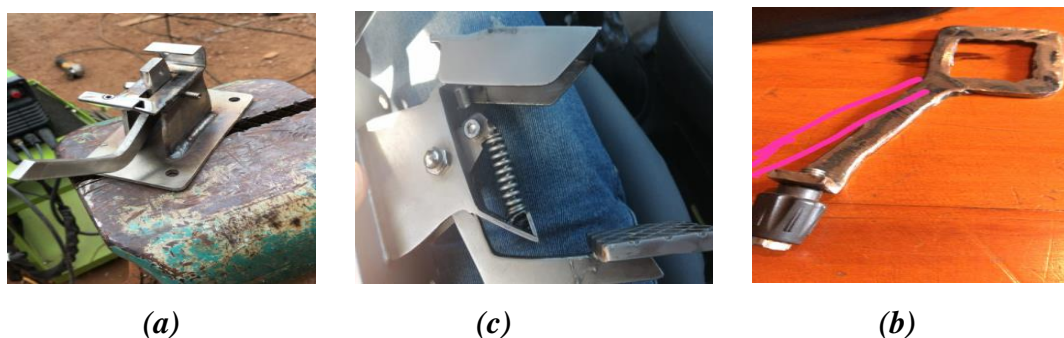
Mecanismo del pedal, (a) Base del soporte, (b) Unión de piezas por medio de soldadura, (c) Acople fijo para tensión
